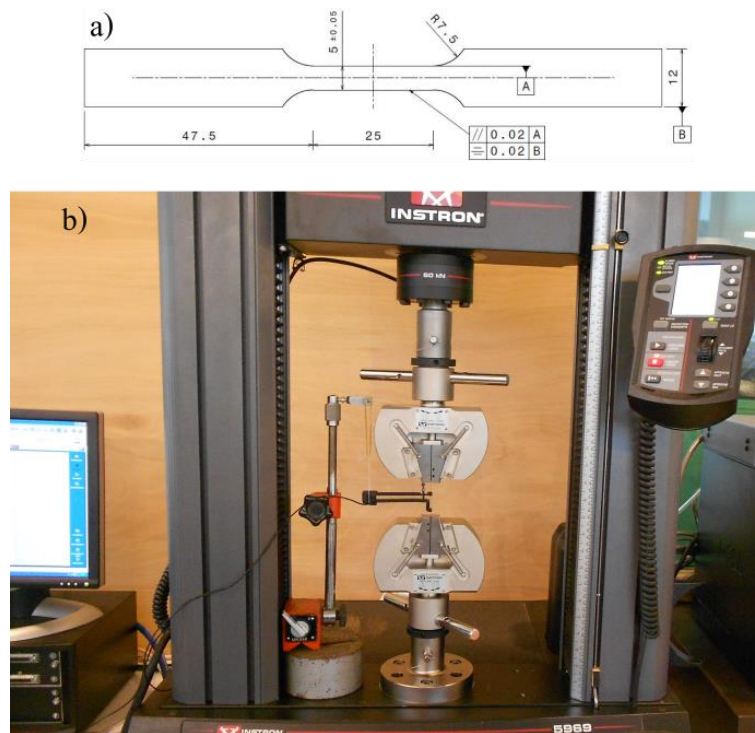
(a) dessin de définition des éprouvettes utilisées, (b) éprouvette montée sur la machine avec le système de suspension de l'extensomètre
